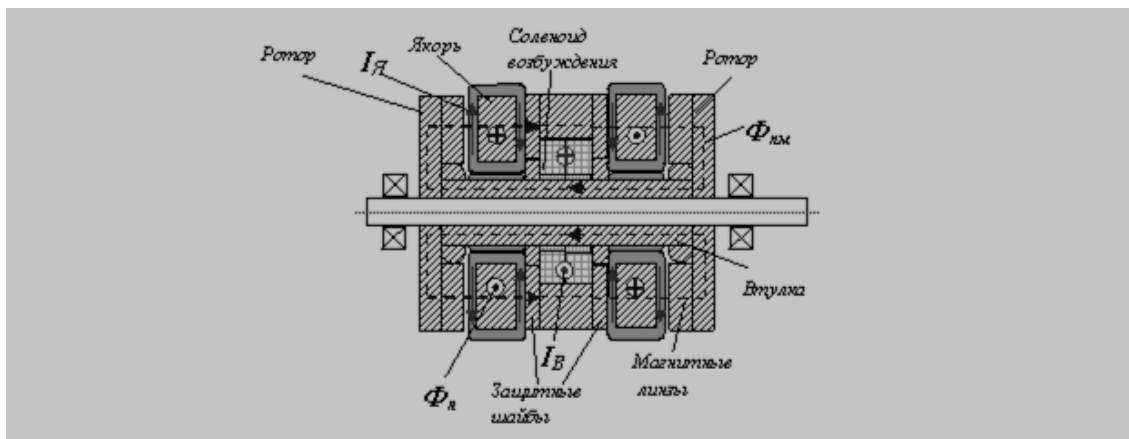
Продольный разрез электродвигателя постоянного тока торцевой конструкции без коллектора и инвертора.
